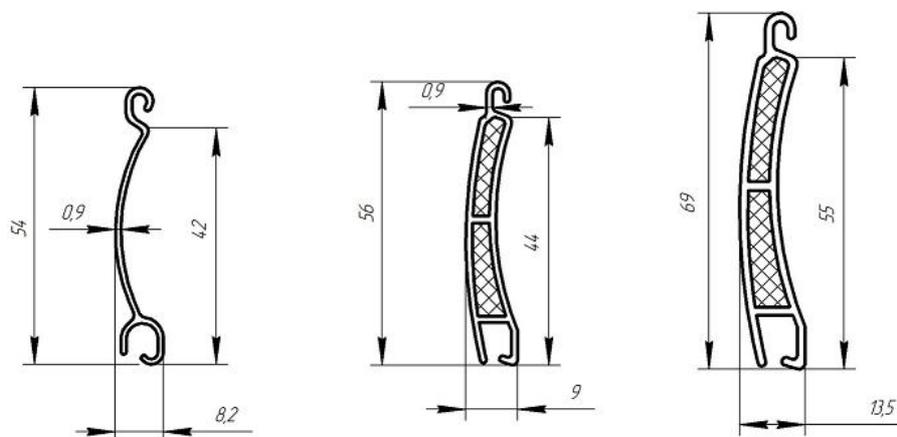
Габаритные размеры ламелей различного исполнения
